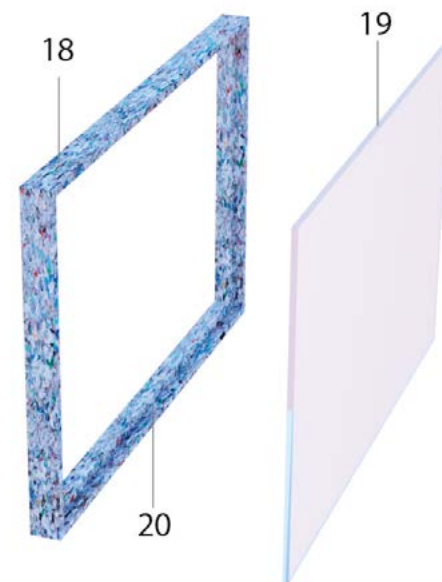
Detalle constructivo 3d puerta de alacena HDPE reciclado con vidrio
